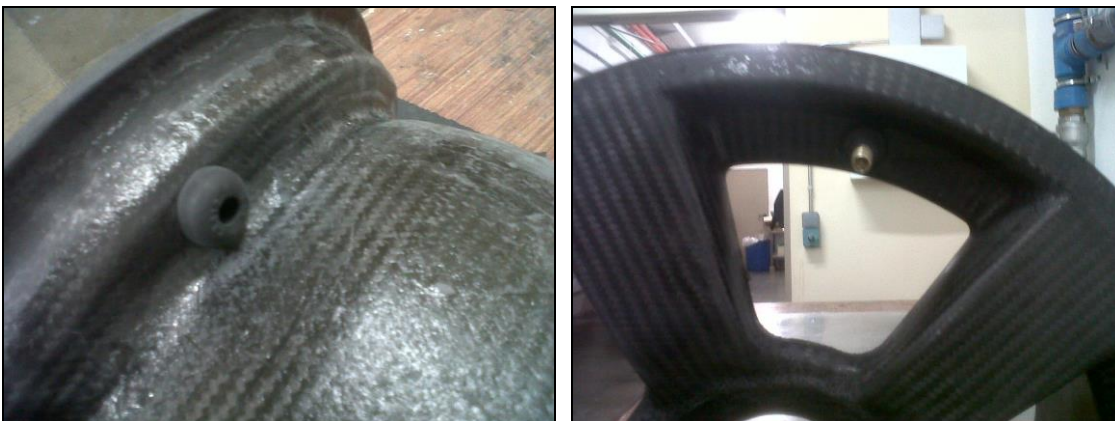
Detalle de la válvula de hinchado colocada en la llanta
